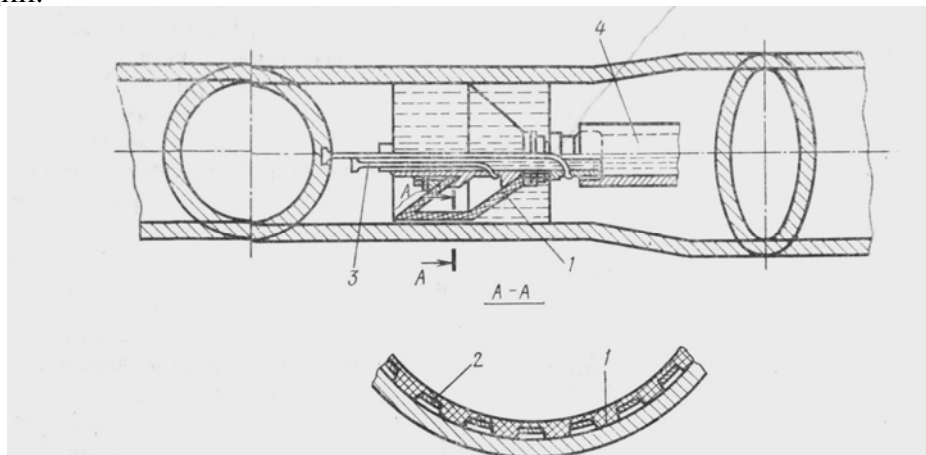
Конструкция нежесткого электрода-инструмента для обработки отверстий с профилем переменного сечения:
